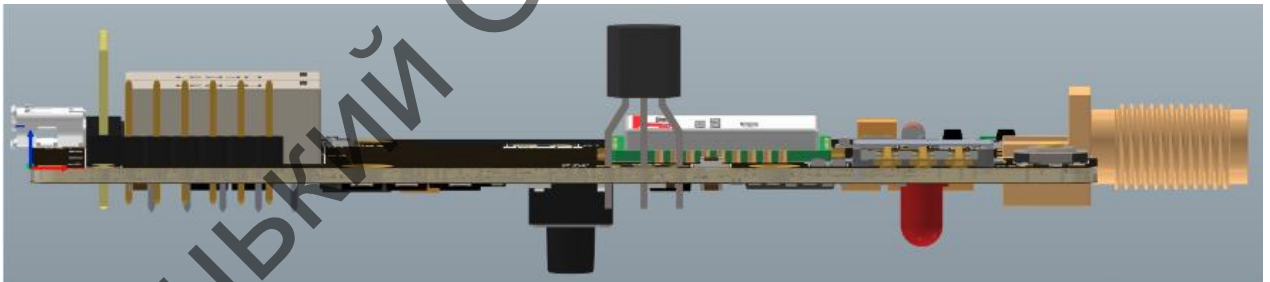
Зовнішній вигляд бокової сторони моделі пристрою
